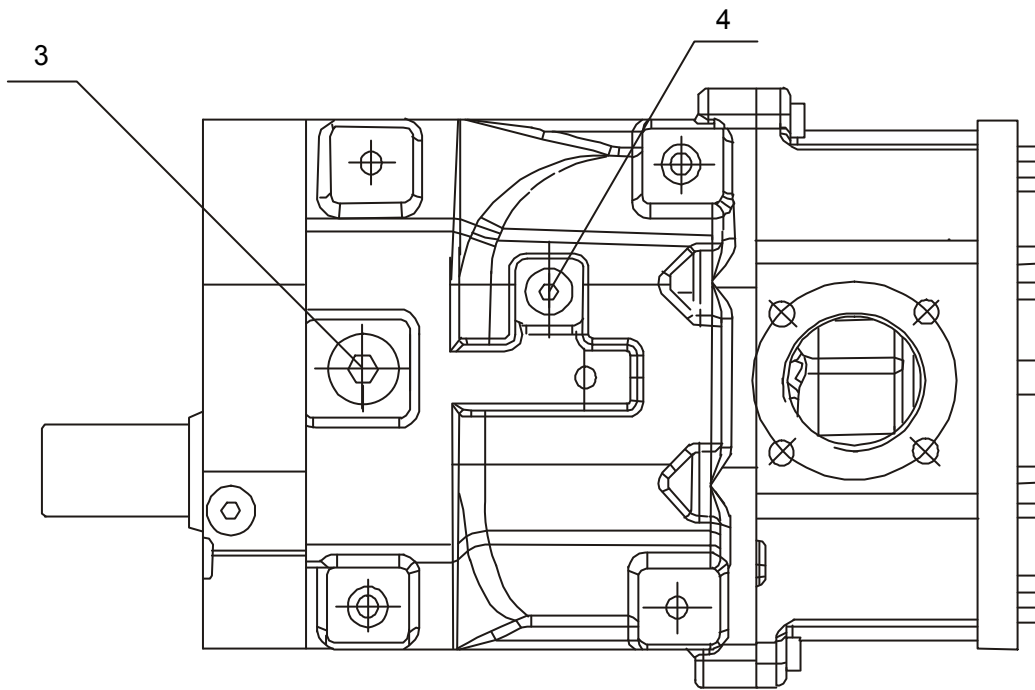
Общий вид компрессорной установки ВК20Е-8(10, 15)-500Д
